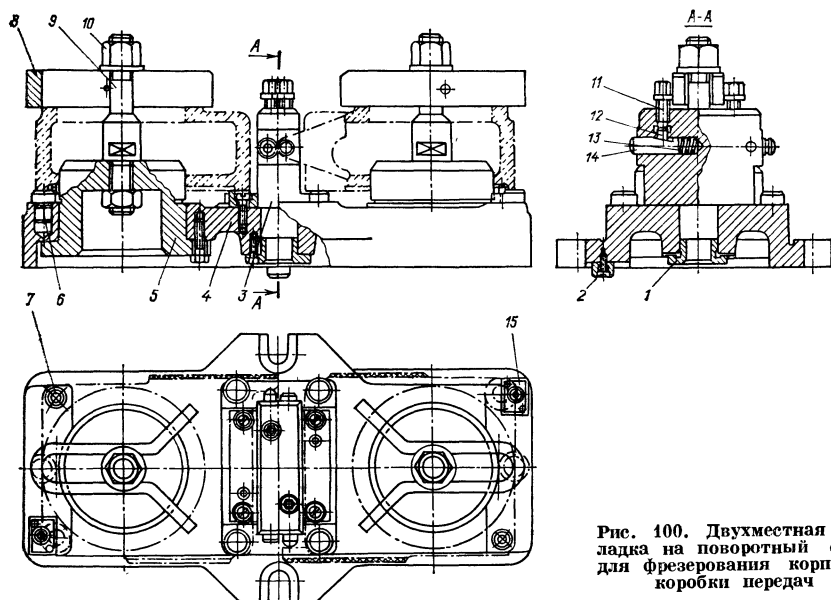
Двухместная наладка на поворотный стол для фрезерования корпусов коробки передач
